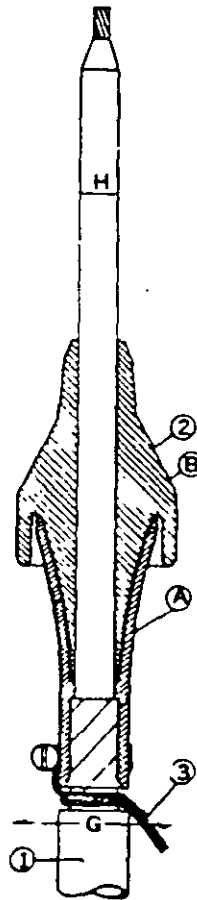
Detalle constructivo de la terminal para uso en interiores (TIP).
